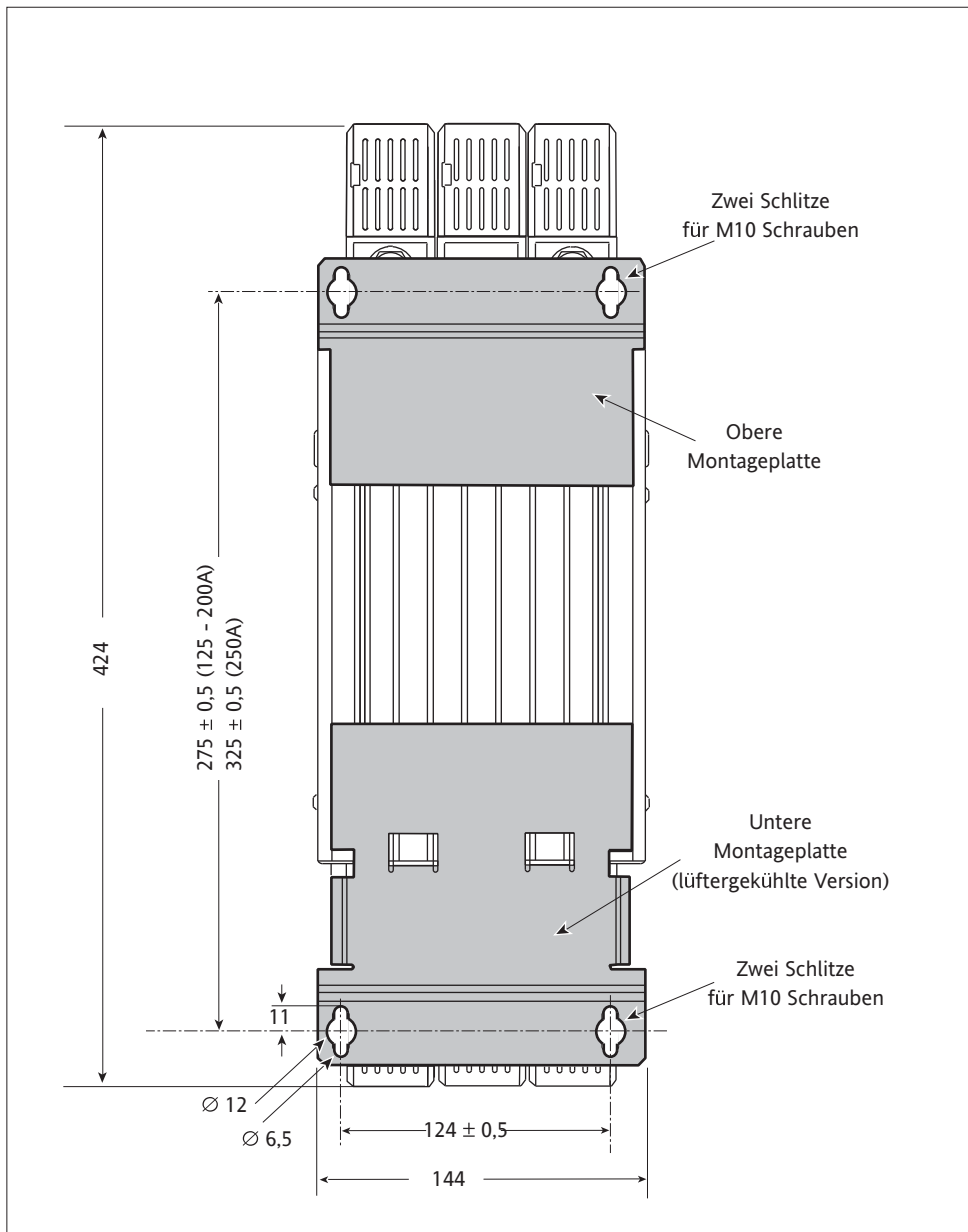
Rückwandmontage für 125A bis 250A (lüftergekühlt, Rückansicht)
